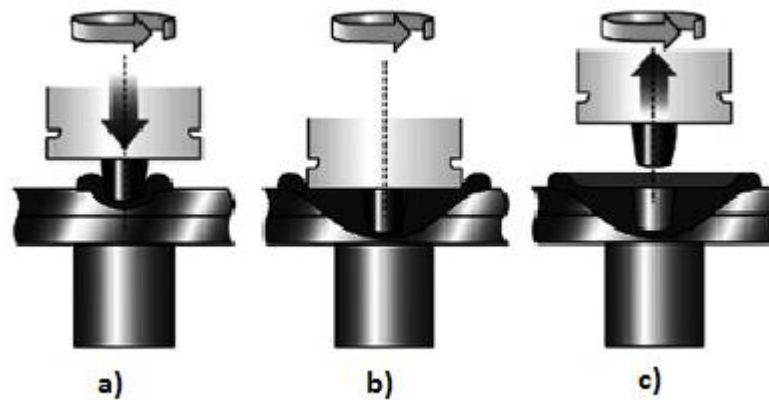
Esquema do processo de *FSSW*- a) fase de penetração; b) fase de soldadura; c) Saída da ferramenta (Zhang, Z., *et al.*, 2011).
